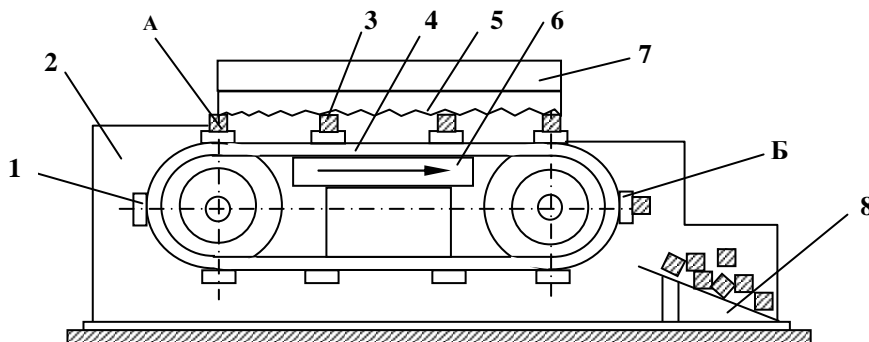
Схема горизонтально-протяжного станка непрерывного действия
